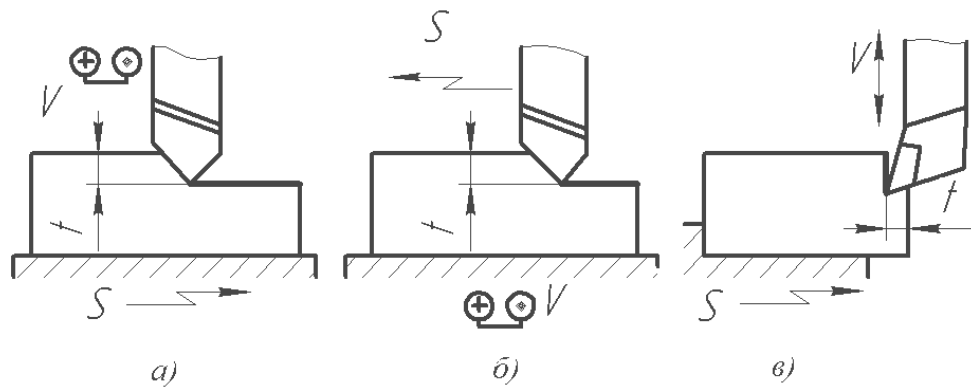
Схеми оброблення площин на верстатах:
